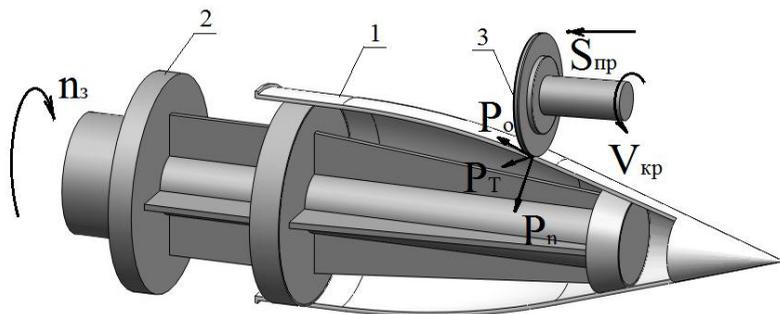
Схема базирования заготовки на операции наружного шлифования изделия: 1 – формируемый контур изделия; 2 – приспособление-оправка, в котором опорными участками служат гетинаксовые втулки; 3 – алмазный круг 1A1 200x10x3x76 A1-315/250-4- M2-01
